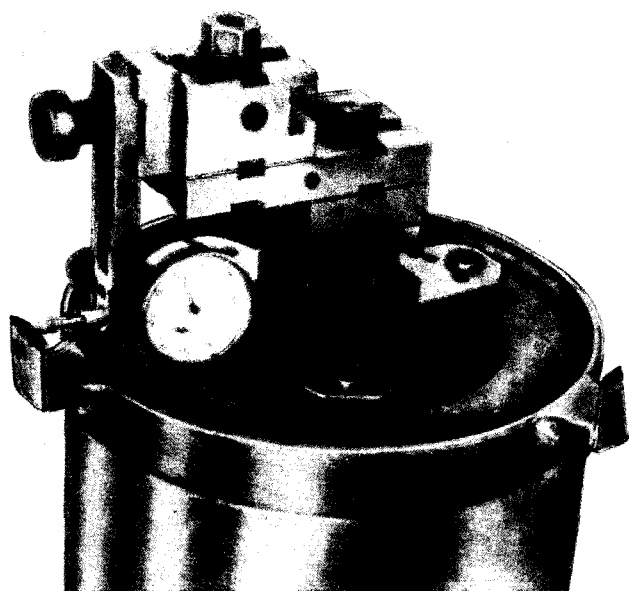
Приспособление для проверки соосности внутренних диаметров цилиндра и наружных лапок
